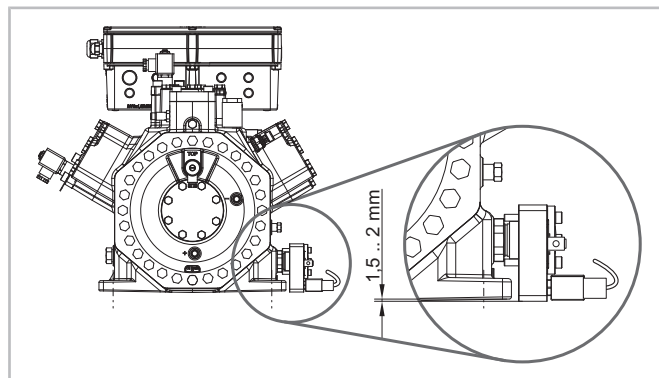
OLM-IQ peut dépasser vers le bas par quelques millimètres.
